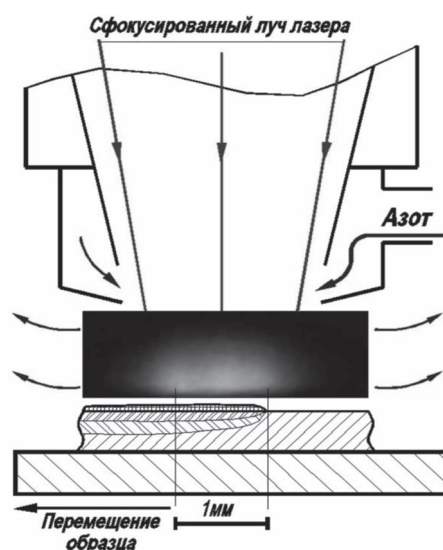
Схема лазерно-плазменной обработки металла с фотографией приповерхностной плазмы оптического пульсирующего разряда
